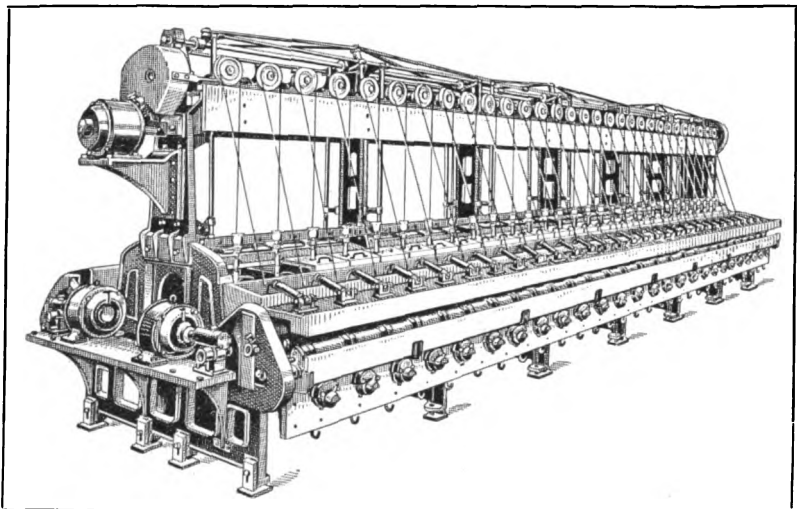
Kunstseide-Spinnmaschine mit elektr. Zentrifugen und Einzelantrieb der Hauptwellen (Spinnzentrifugen-Schalter älterer Ausführung).
